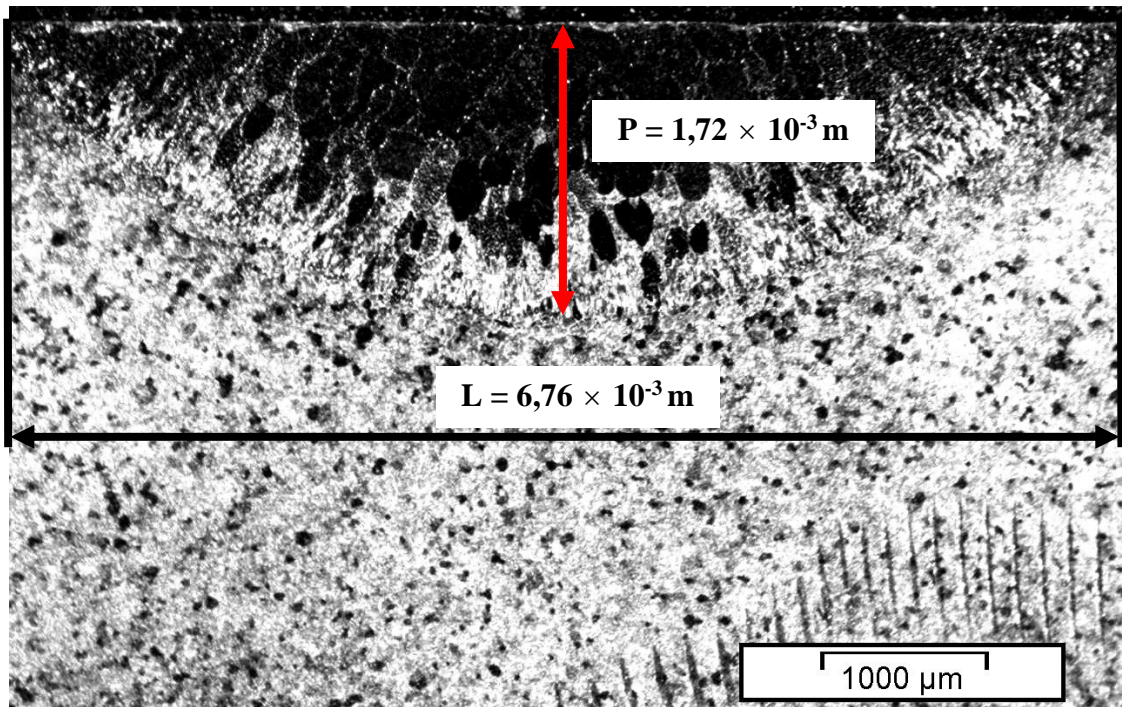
Largura e penetração do cordão de solda para condição de $t+ = 11 \text{ ms}$.
